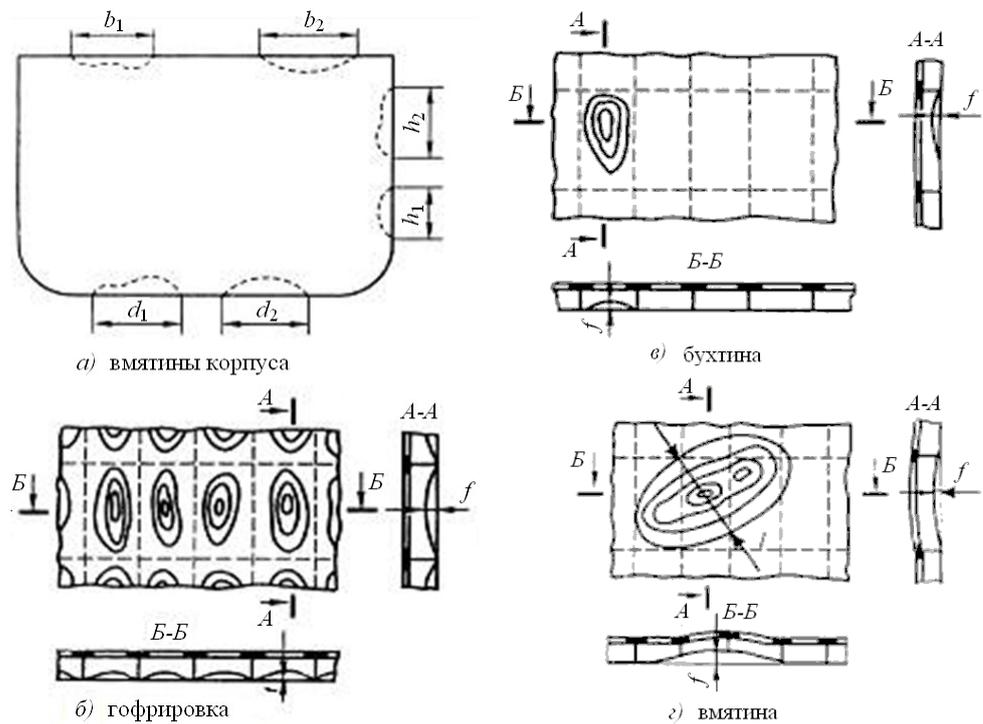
Виды дефектов обшивки корпусов судов [12, 13]
